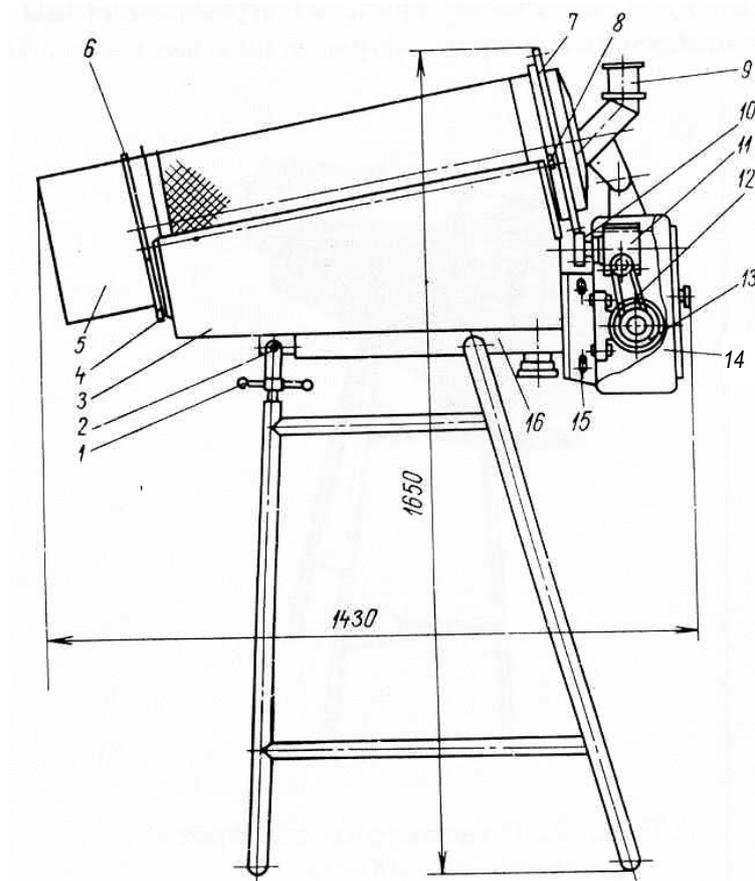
Общий вид отделителя сыворотки марки РЗ-003: 1 – регулировочный винт; 2 – шарнир; 3 – поддон; 4, 8 – ролики; 5 – барабан; 6, 7 – кольца; 9 – патрубок; 10 – ведущая шестерня; 11 – червячный редуктор; 12 – ременная передача; 13 – электродвигатель; 14 – привод; 15 – болт; 16 – скоба
